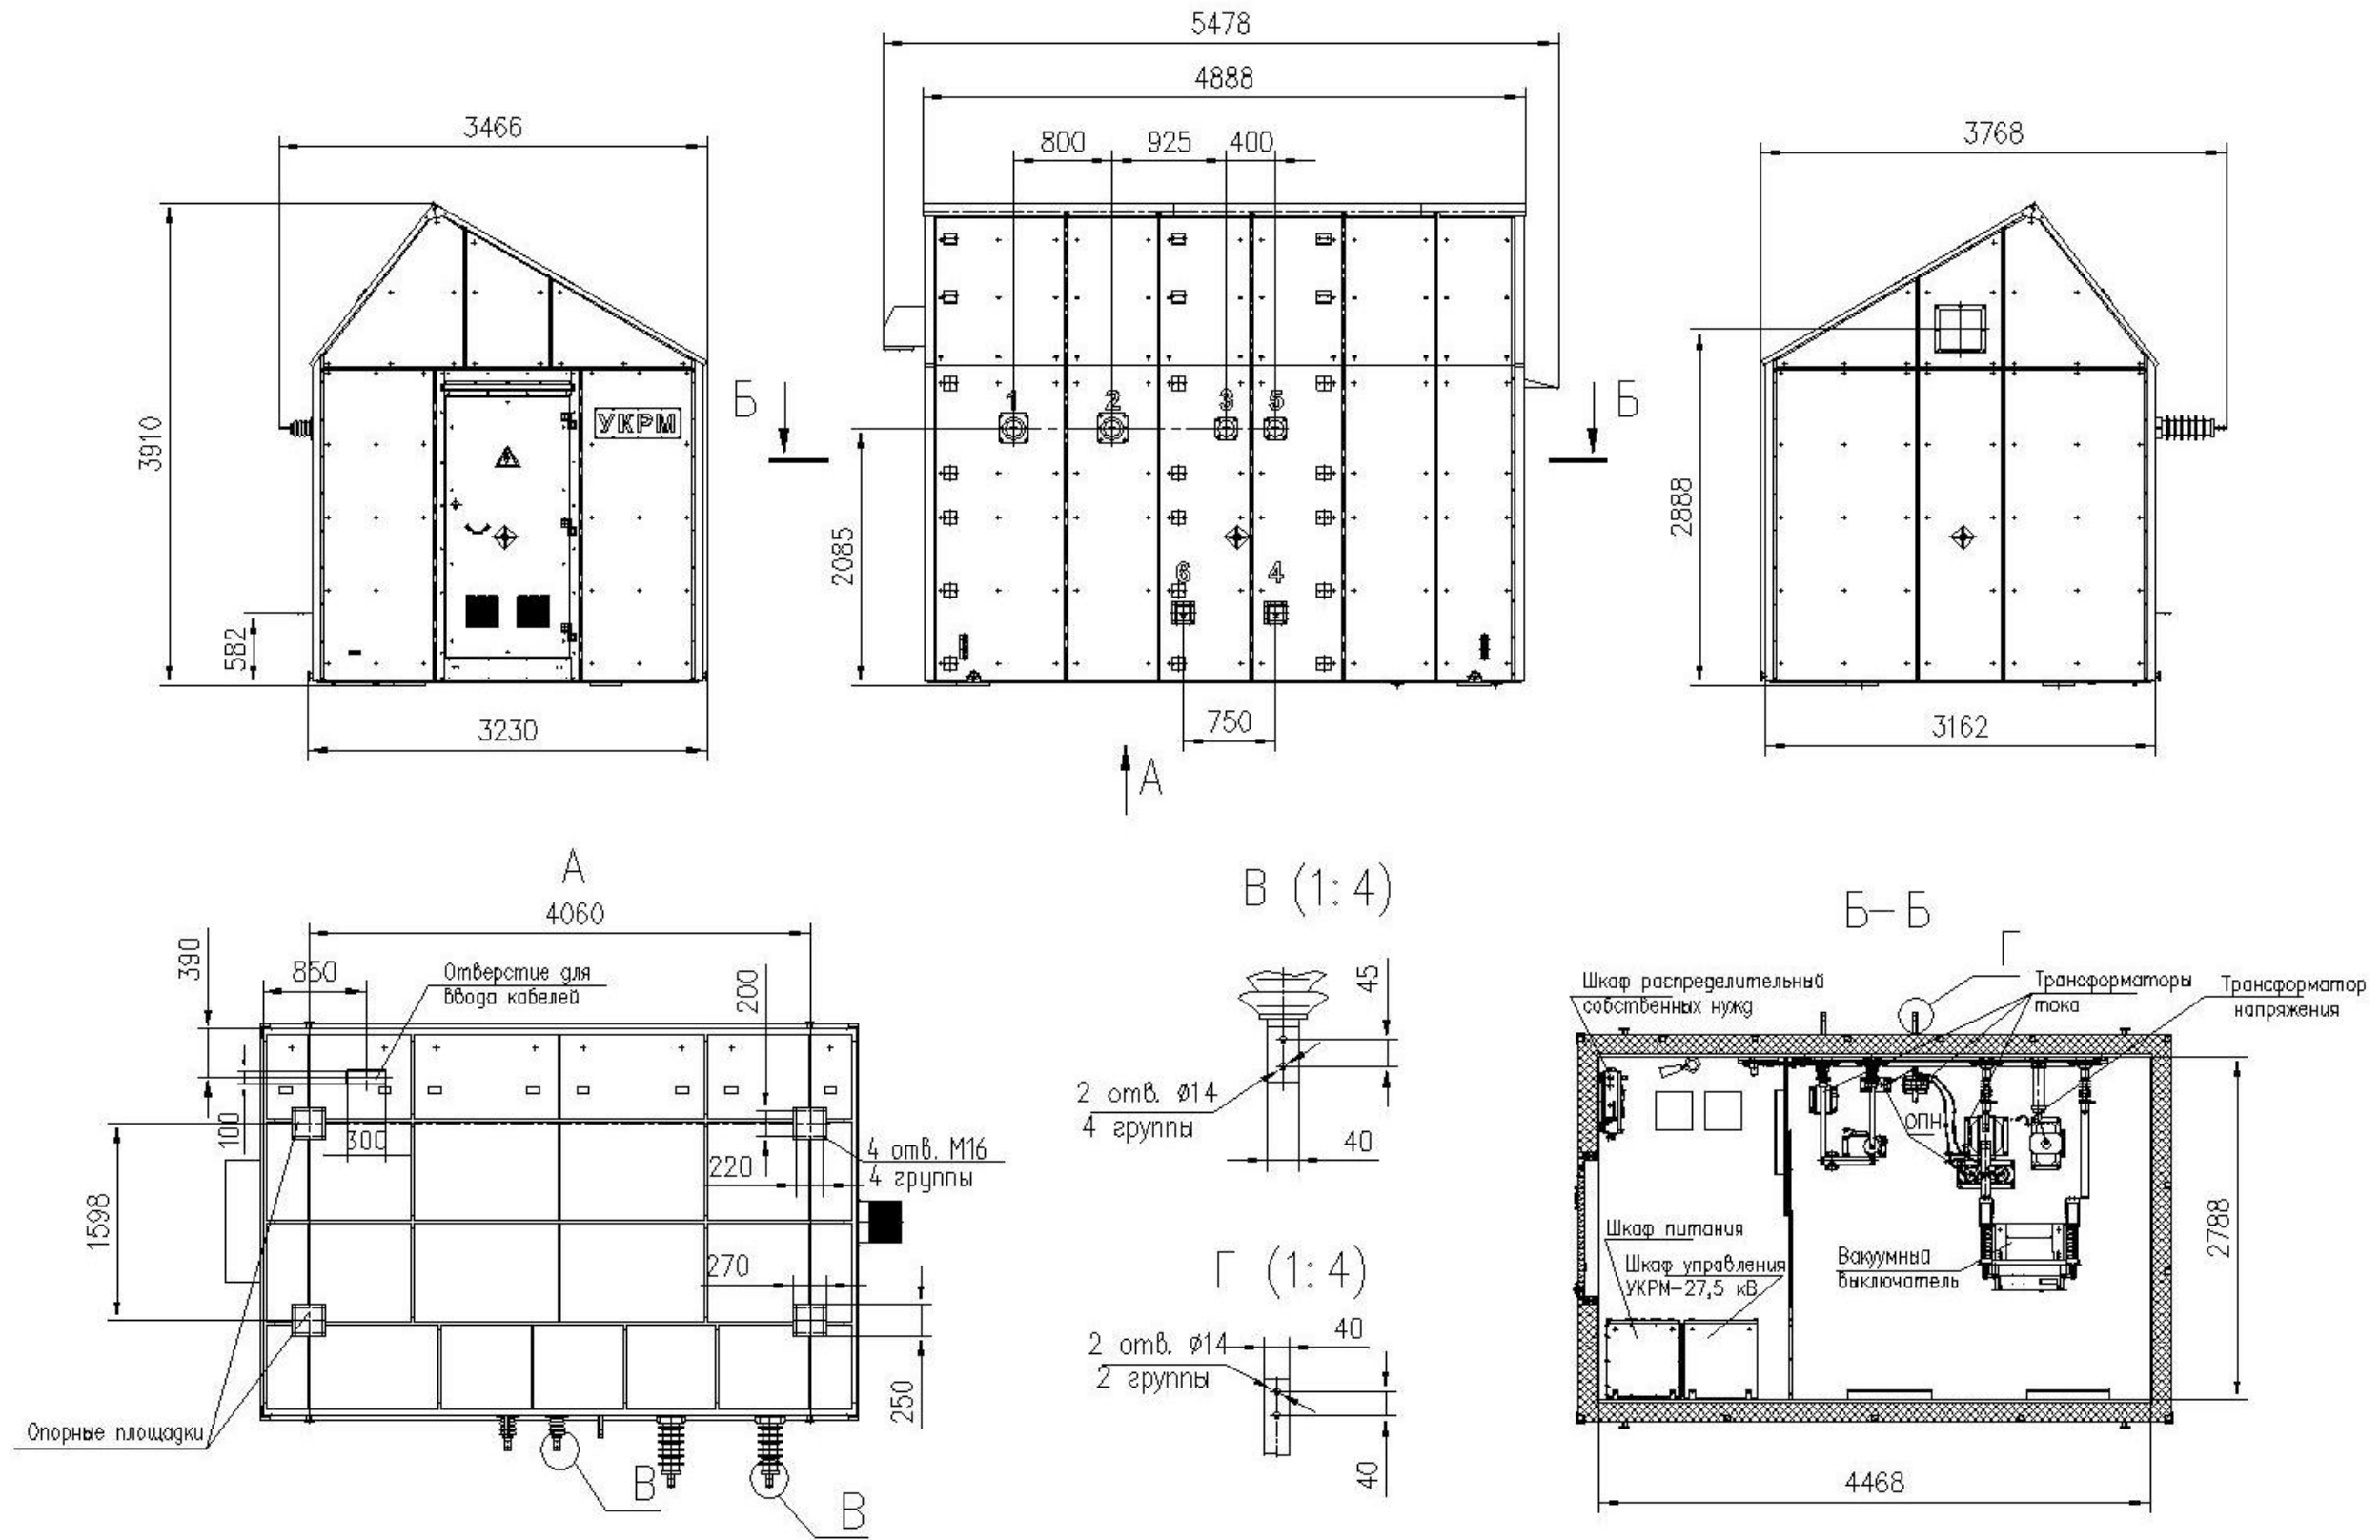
Габаритный чертеж модуля управления УКРМ-27,5 кВ типоразмером 4,8 м
